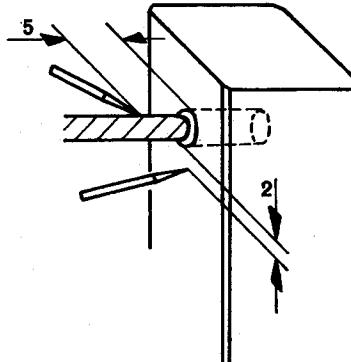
Contact soudé. FIG. C2d. — Connexion latérale scellée ou moulée. FIG. C2e. — Connexion par étrier soudé ou rivé.
